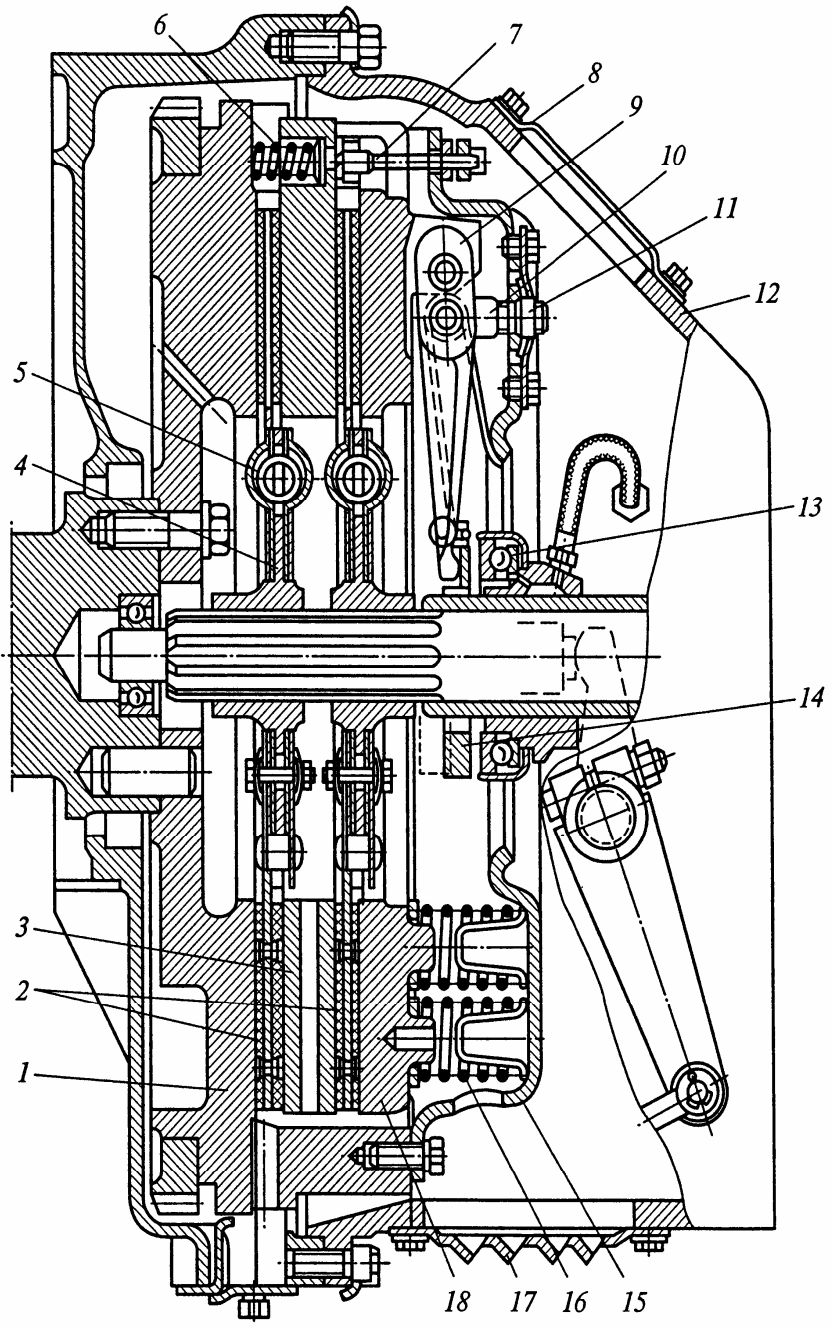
Сцепление грузовых автомобилей МАЗ:
